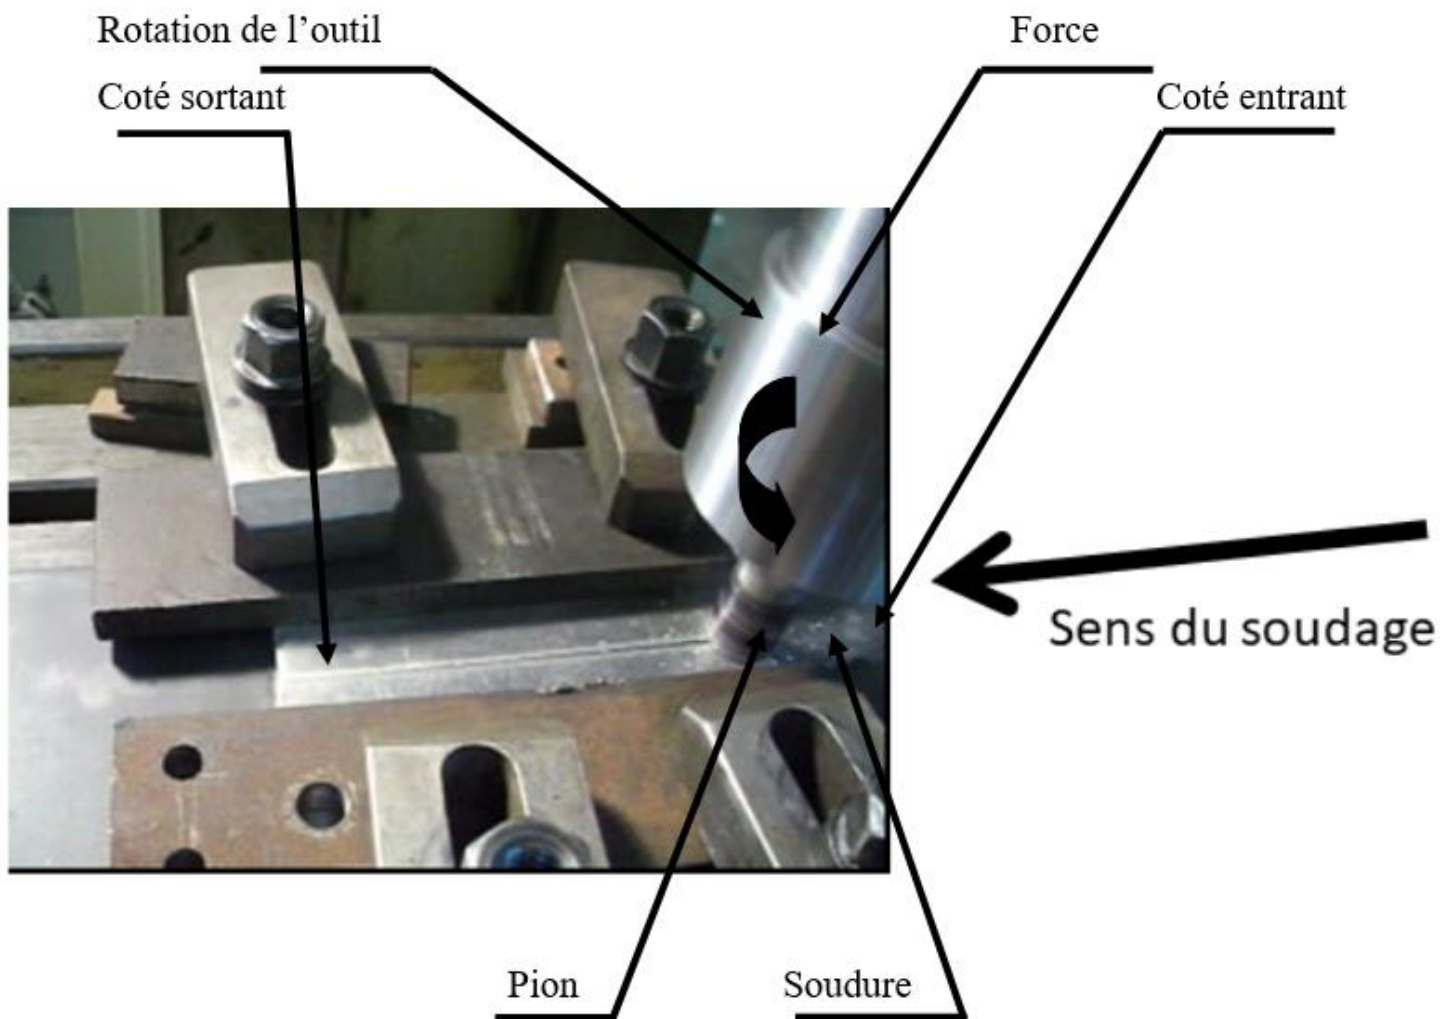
Schématisation du côté avance et recul lors du soudage FSW
